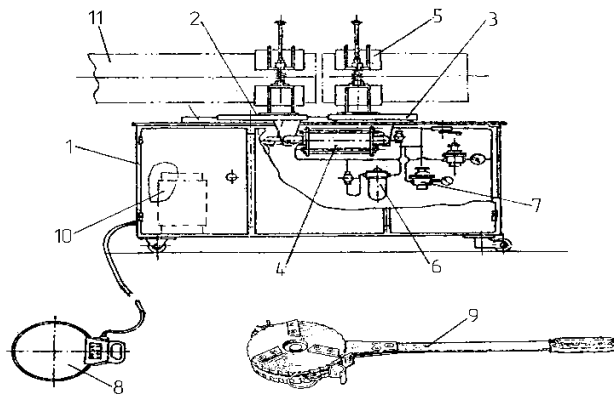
Станок для контактной сварки полимерных труб с пневмоприводом: 1 - каркас; 2 - каретка подвижная; 3 - каретка неподвижная; 4 - пневмоцилиндр; 5 - зажим для труб; 6 - пневмосистема станка; 7 - регулятор давления сжатого воздуха (редуктор); 8 - нагреватель; 9 - устройство торцовочное; 10 - трансформатор; 11 - свариваемые трубы
